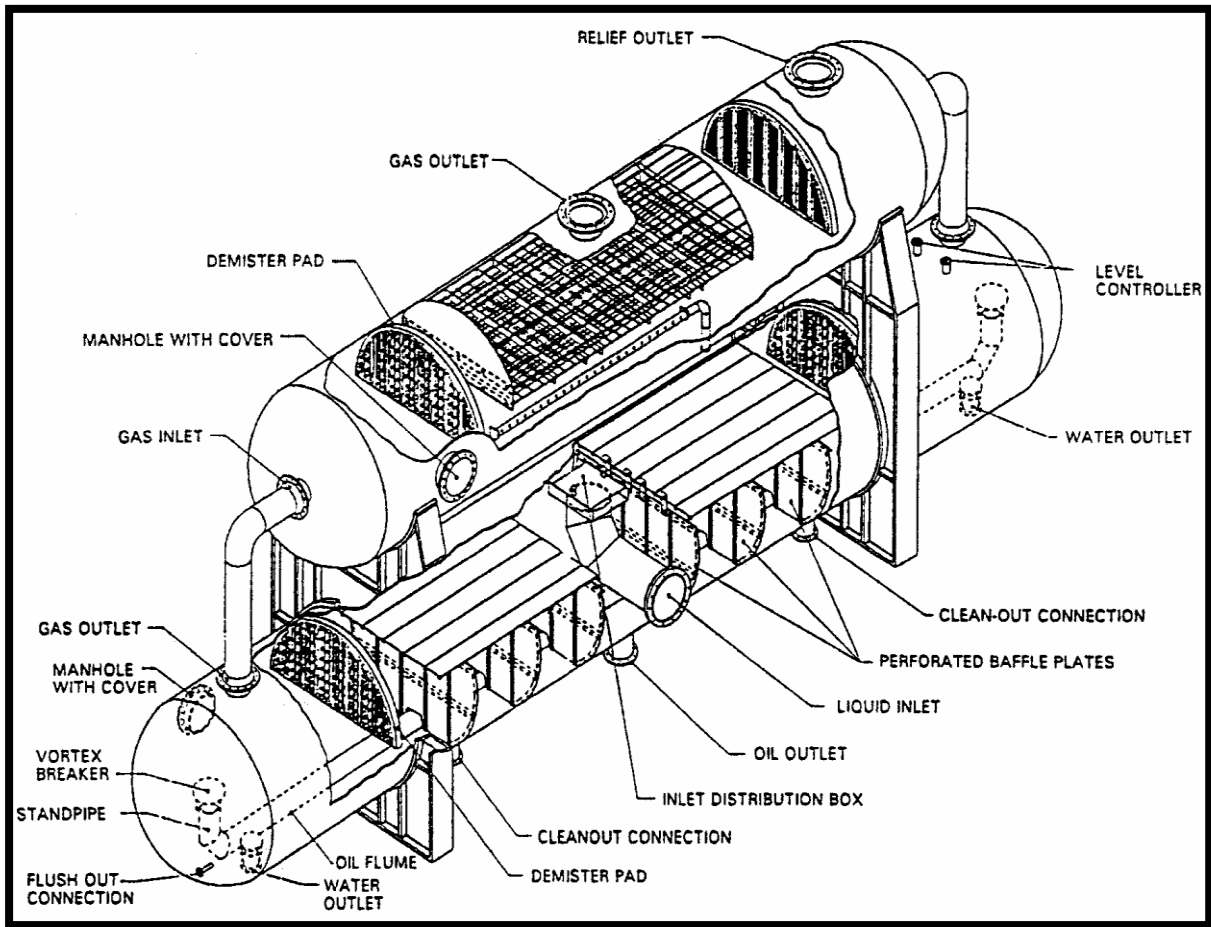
Vue écorchée d'un séparateur triphasique horizontal à deux tubes [1]
